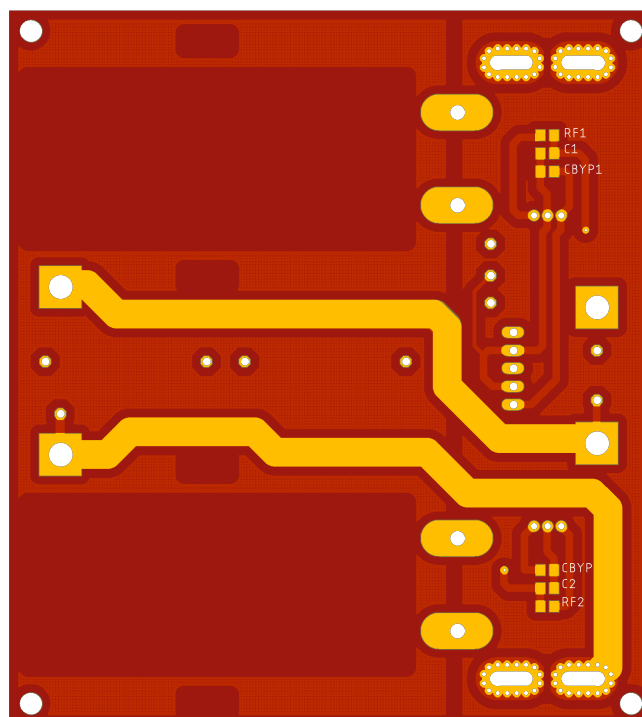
Vista previa del PCB en la capa inferior antes de fabricar.
